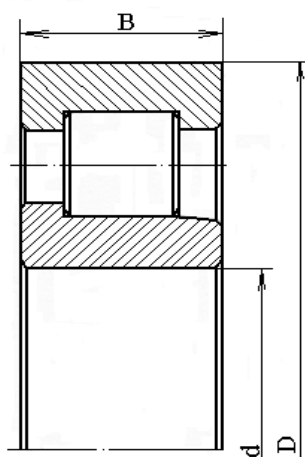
Подшипник роликовый радиальный, с короткими цилиндрическими роликами
